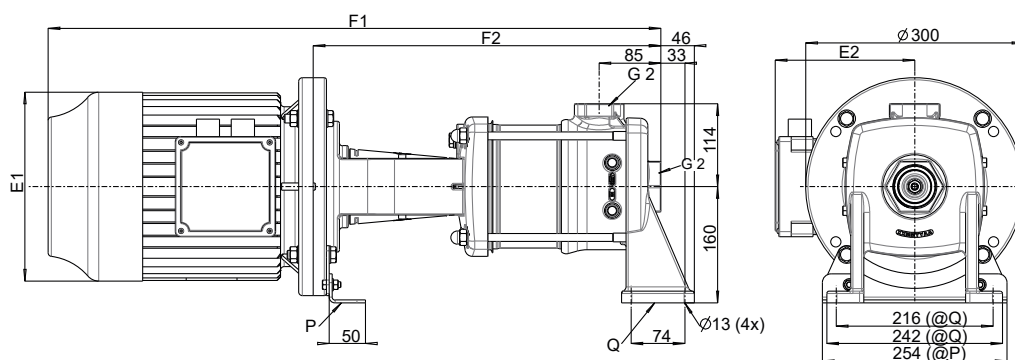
Abmessungen und Anschlüsse Movitec H(S)I 15 mit Motor V1
